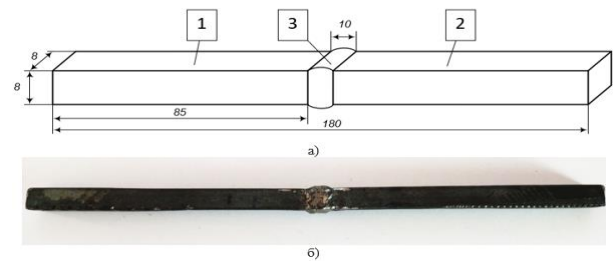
Експериментальний зразок: а) схематичний вигляд експериментального зразка (1, 2 – заготовки зі сталевго прутка; 3 – зварний шов); б) загальний вигляд зразка
